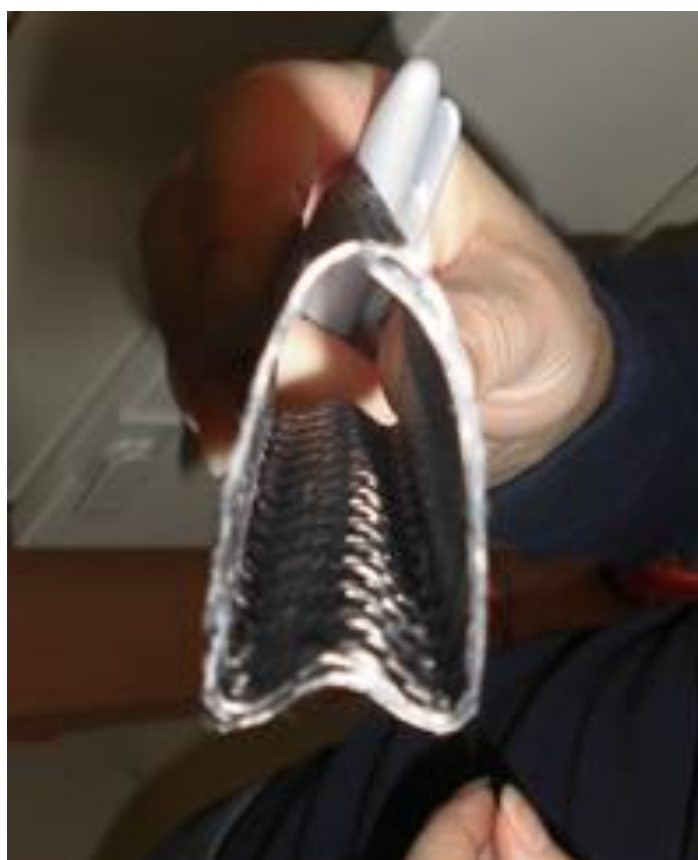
Spodní díl formy s vytvrzeným prepregem
